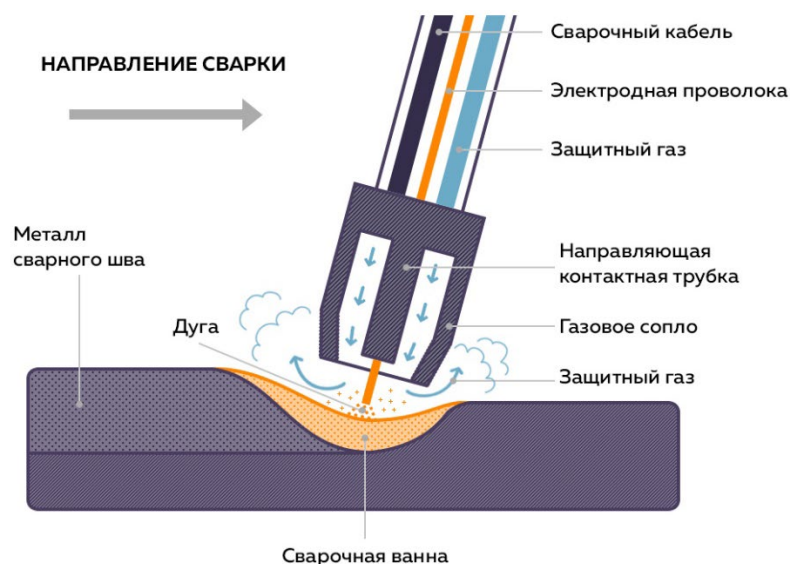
Схема выполнения механизированной сварки в защитных газах
